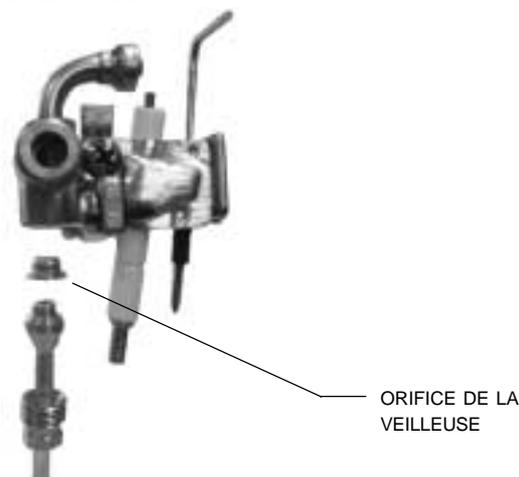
Brûleur et orifice de la veilleuse (assemblage illustré sans le capuchon de la veilleuse)
